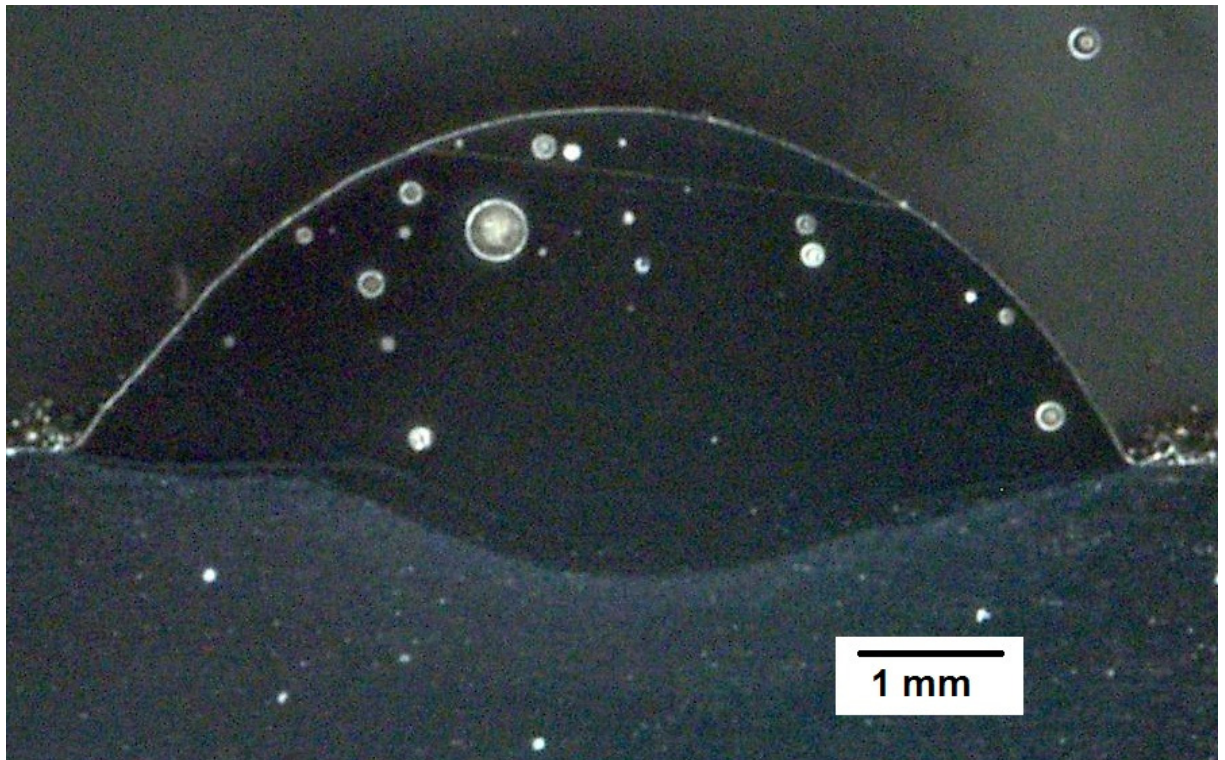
Querschliff durch die Auftragschweißspur mit einer Bearbeitungsgeschwindigkeit $v=20$ mm/s
